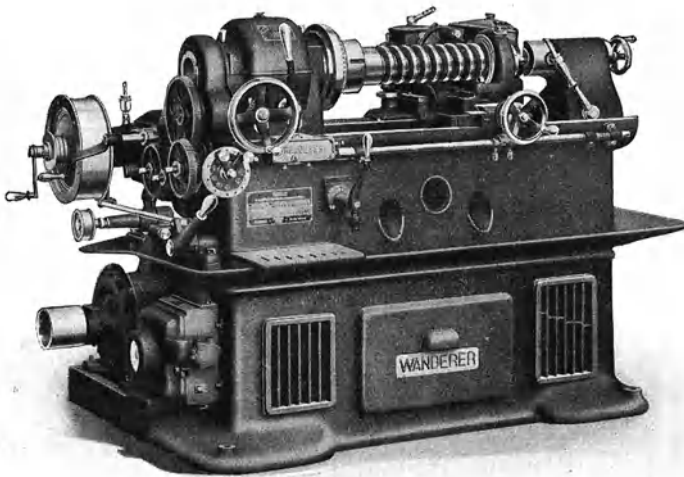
Die Universalgewindefräsmaschine von Wanderer.
